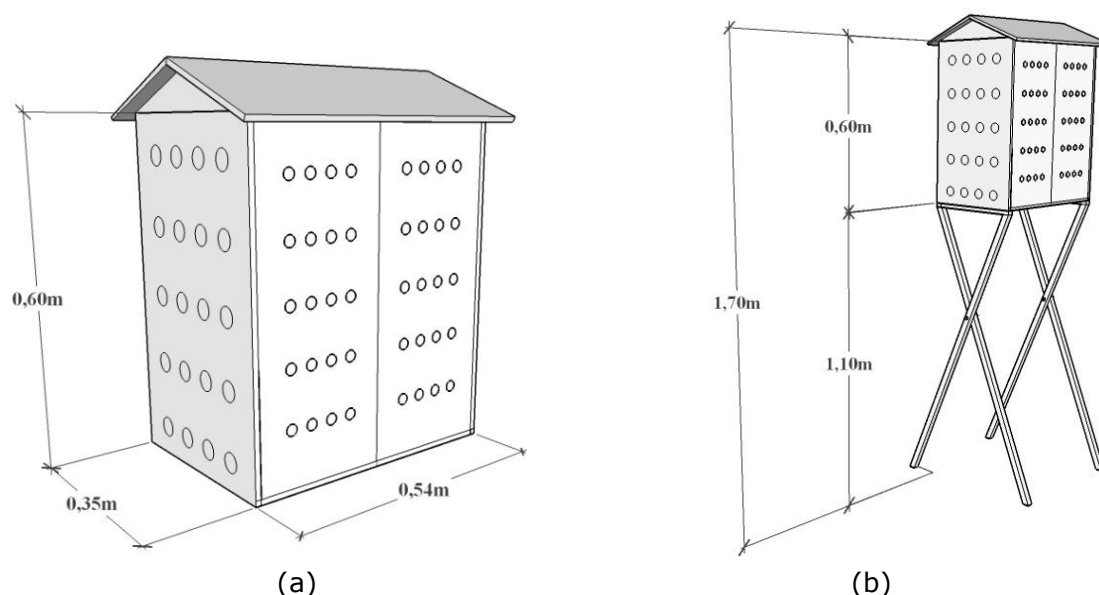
Dimensões do abrigo de madeira (a) abrigo; (b) abrigo com suporte
